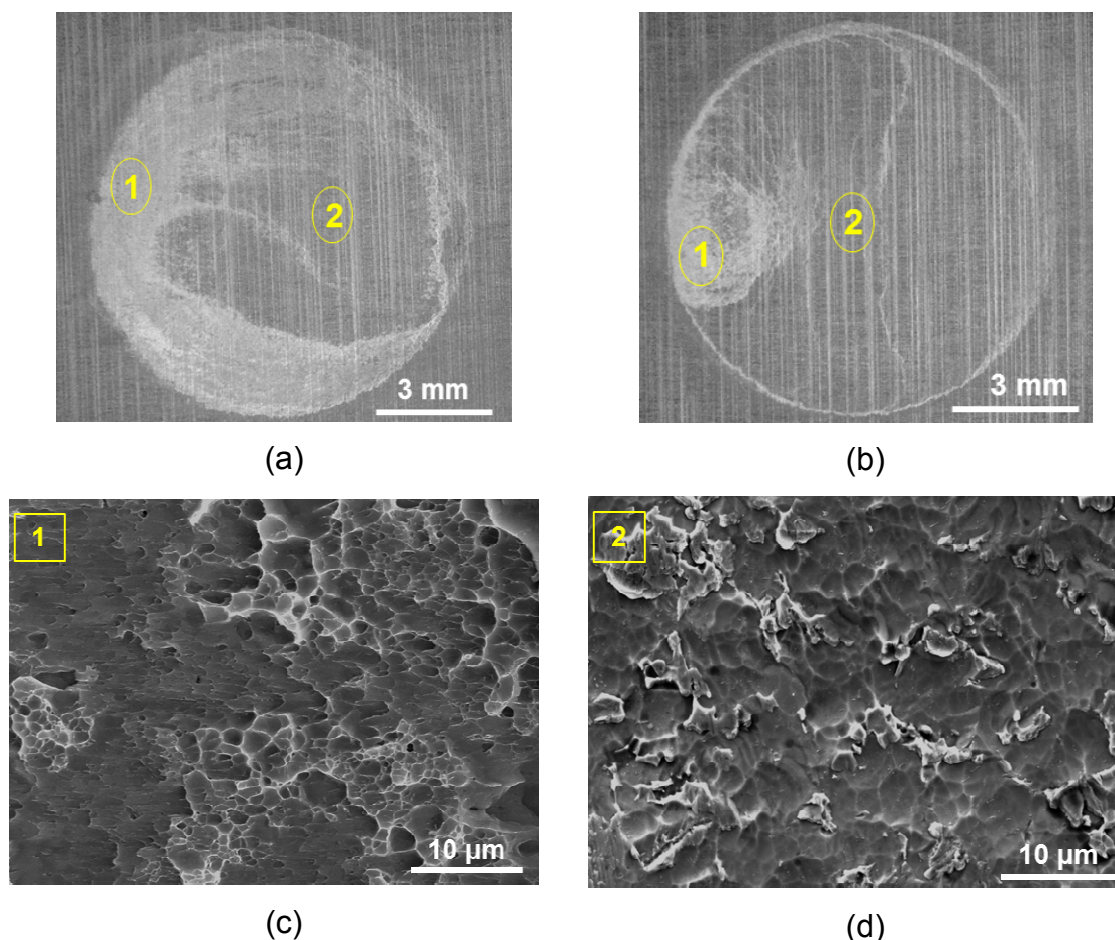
Superfície de fratura da junta AA6181-T4/Ti6Al4V solicitada por cisalhamento para as condições de soldagem 5 (a) e 8 (b). Detalhe da superfície de fratura das regiões 1 (c) e 2 (d).
